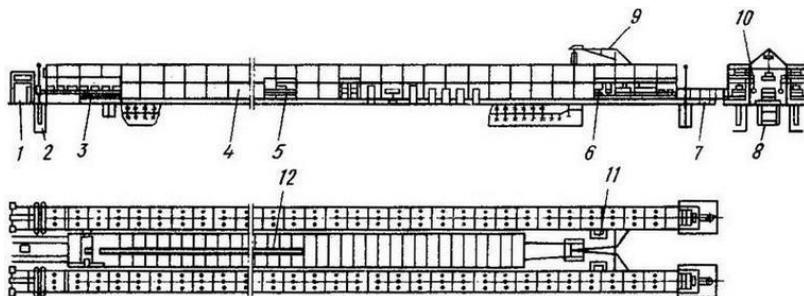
Схема литейно-подвялочного конвейера СМ-462А: 1 – гидротолкатель верхний; 2 – гидроподъемник; 3 – механизм слива шликера; 4 – камера; 5 – механизм заливки шликера; 6 – тележки; 7 – гидротолкатель нижний; 8 – подвялочный конвейер; 9 – пневмоподъемник; 10 – монорельс уборки отходов; 11 – механизм съема изделий; 12 – конвейер возврата воронок и колышков
